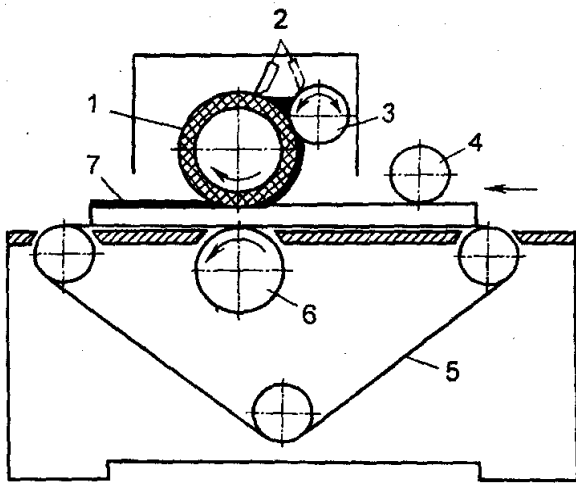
Схема вальцювального верстата, що наносить ЛФМ:
